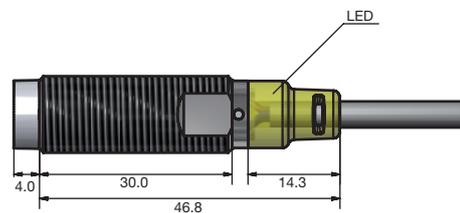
Kurze Ausführung, Nicht bündiger Einbau, Kabel
